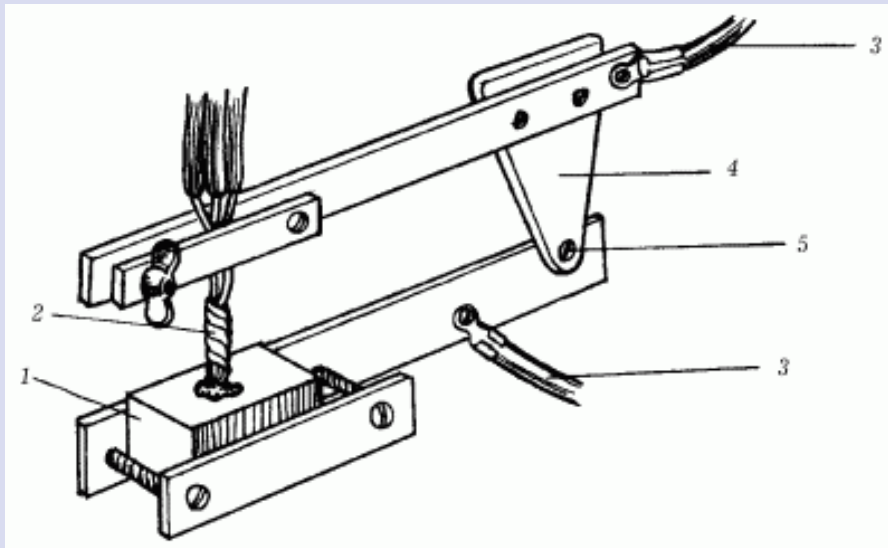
Шарнирный зажим для соединения проводов способом сварки: 1 – угольный электрод; 2 – скрутка из жил; 3 – жилы для подключения к сварочному трансформатору; 4 – изоляционная пластина; 5 – шарнирное соединение.
